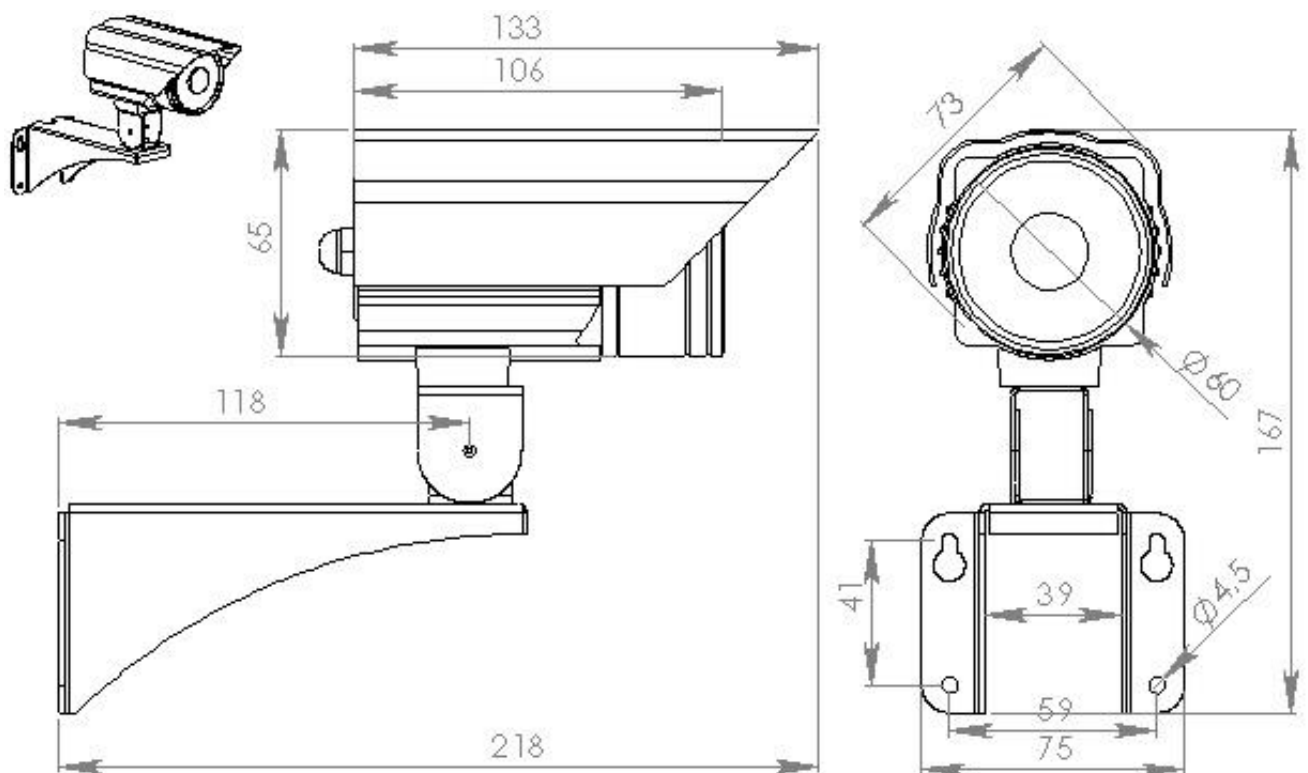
Габаритні креслення VL-8739D[5]
